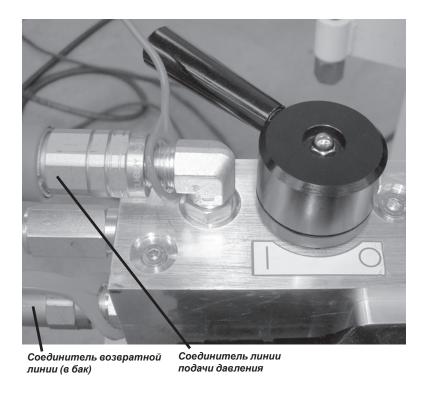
Соедините гидравлические шланги к двигателю, см. изображение.
